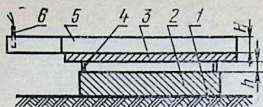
Принципиальная схема сварки взрывом:
